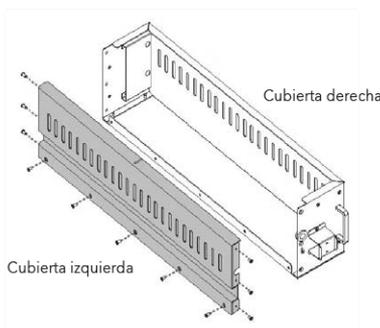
Instalación de baterías 2: retire la cubierta izquierda
